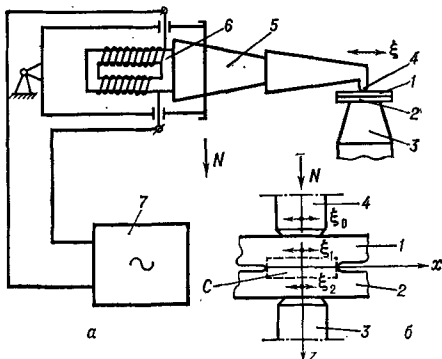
а — схема установки для ультразвуковой сварки с продольными колебаниями; б — область сварки с выделенной пунктиром зоной сварки С; 1, 2 — свариваемые детали; 3 — опора; 4 — сварочный наконечник; 5 — волновод-концентратор продольных колебаний; 6 — магнитострикционный преобразователь; 7 — генератор электрических колебаний.
